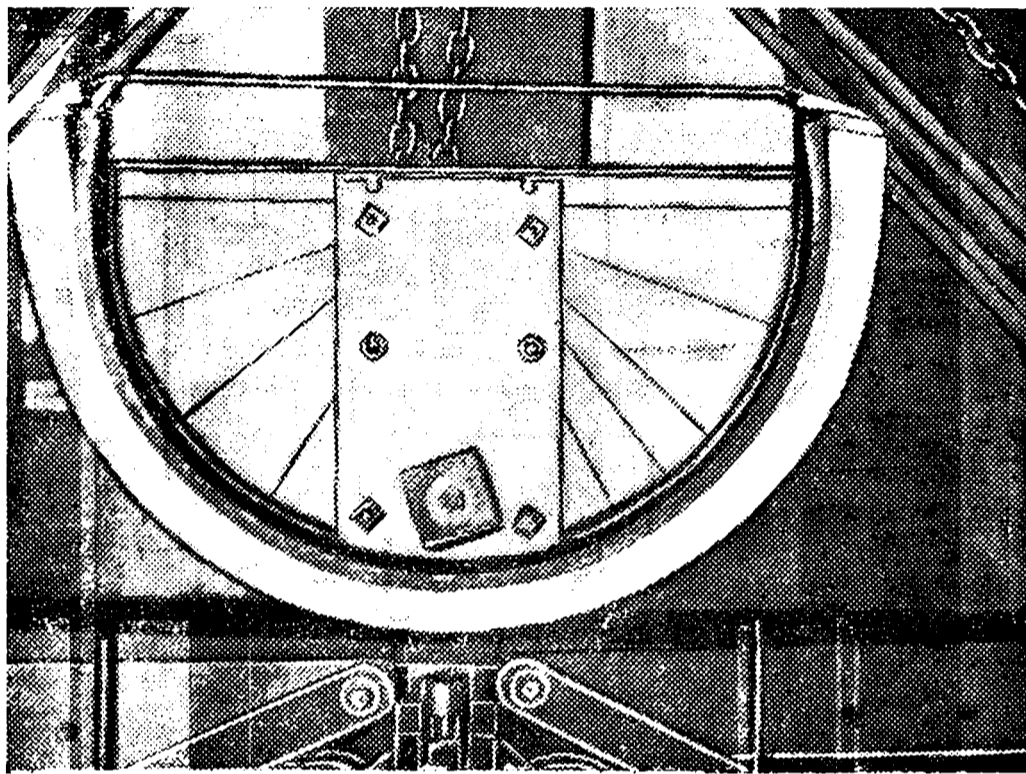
Согнутый хвойный полуобод перед съемкой его со станка
